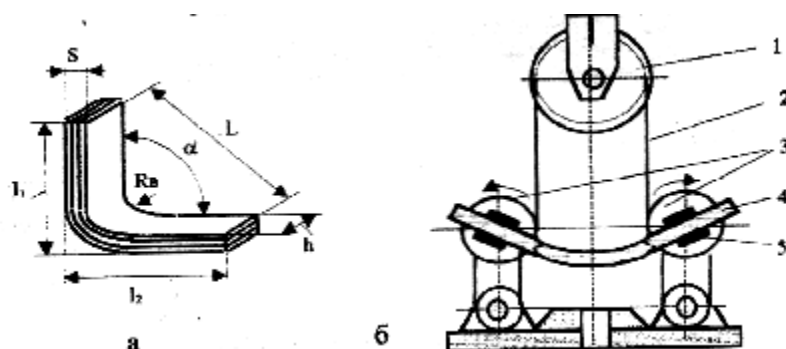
Образец (а) и схема испытания (б) гнutoкeенных заготовок на изгиб: 1 - блок уравнительный; 2 - канат; 3 - блоки закрепления; 4 - образец; 5 - зажимные губки.
